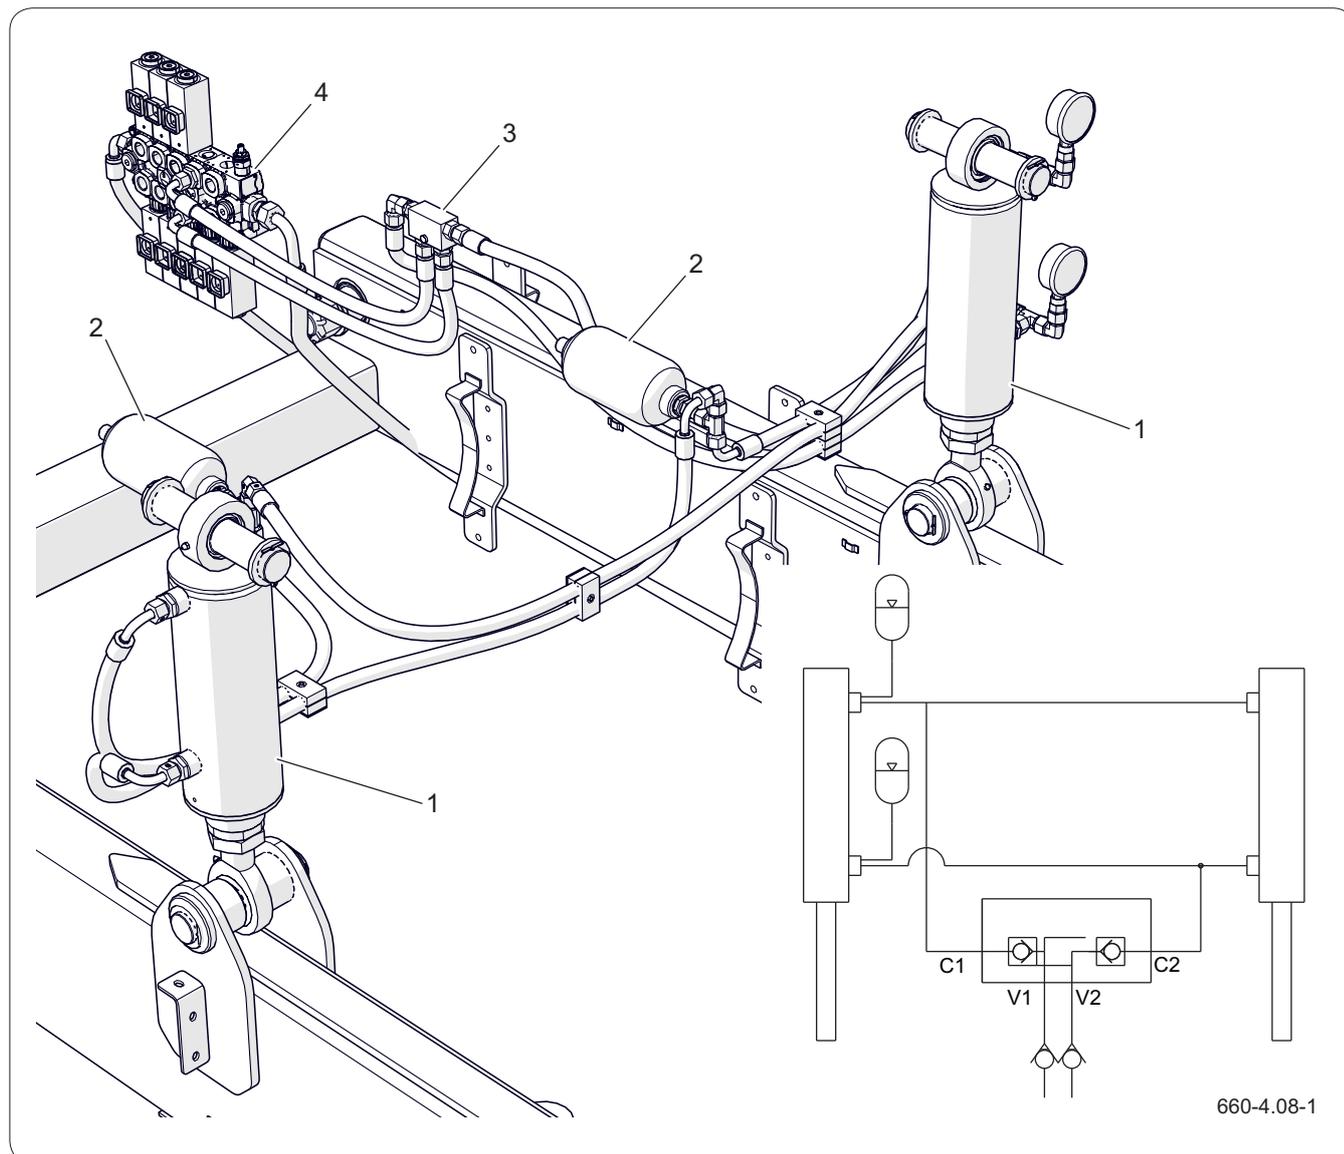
Конструкция и схема гидравлической установки дышла
